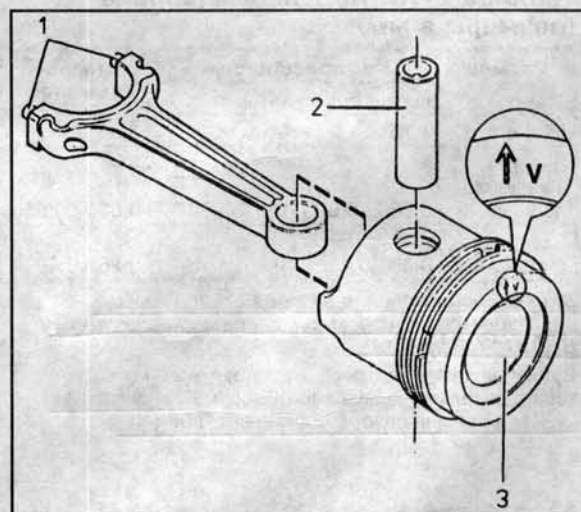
Поршень и шатун двигателя В172, обозначения на днище поршня
